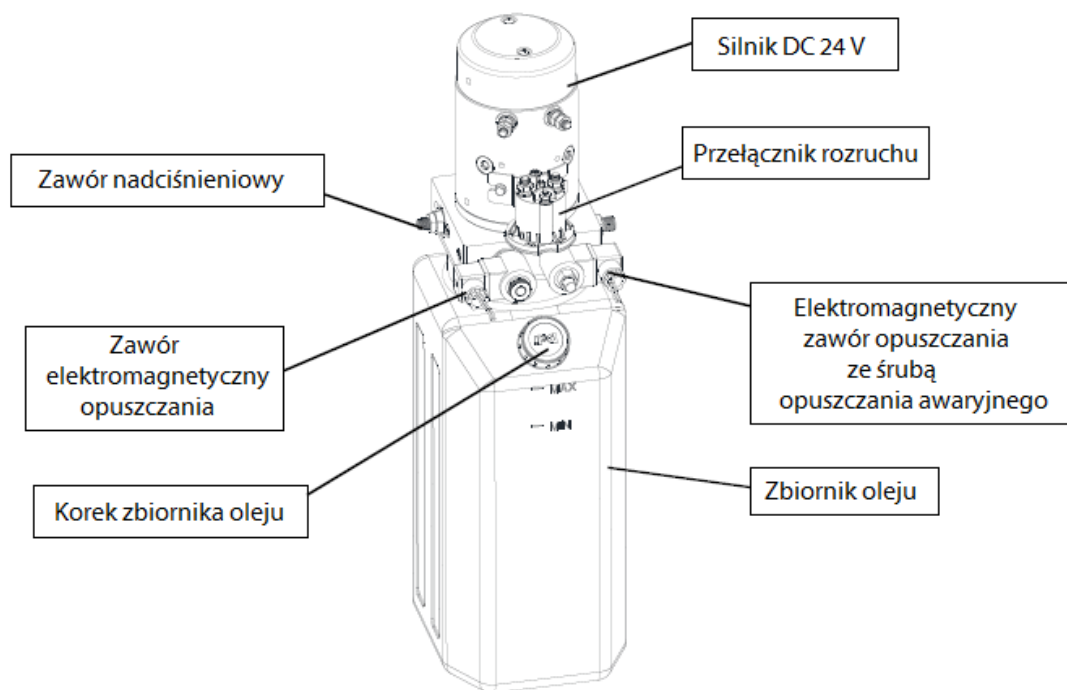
SCHEMAT KOLUMNY 8,5 T
